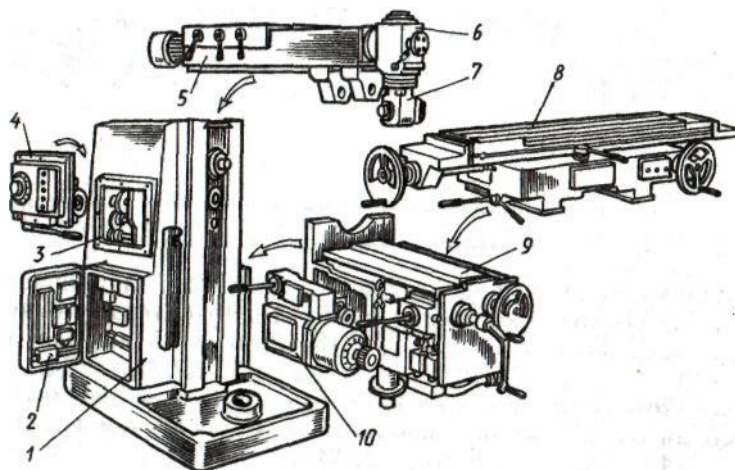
Основные узлы станка мод. 6P82Ш:
